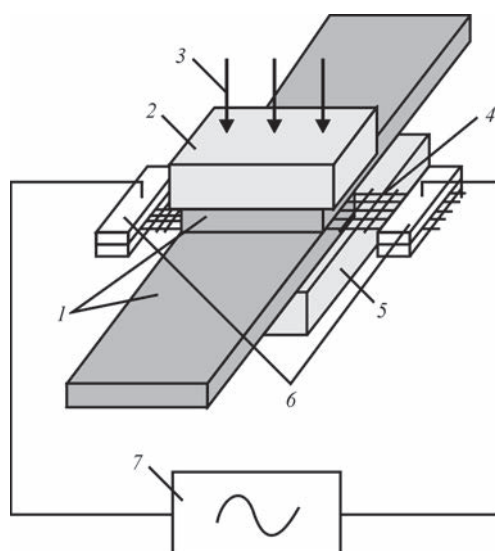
Схема процесса сварки закладным элементом: 1 — образцы; 2 — прижим; 3 — рабочее давление; 4 — закладной элемент; 5 — основание; 6 — электроконтакты; 7 — источник питания
